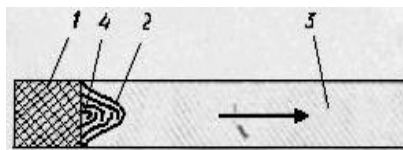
Поверхня втомного руйнування зуба шестерні
